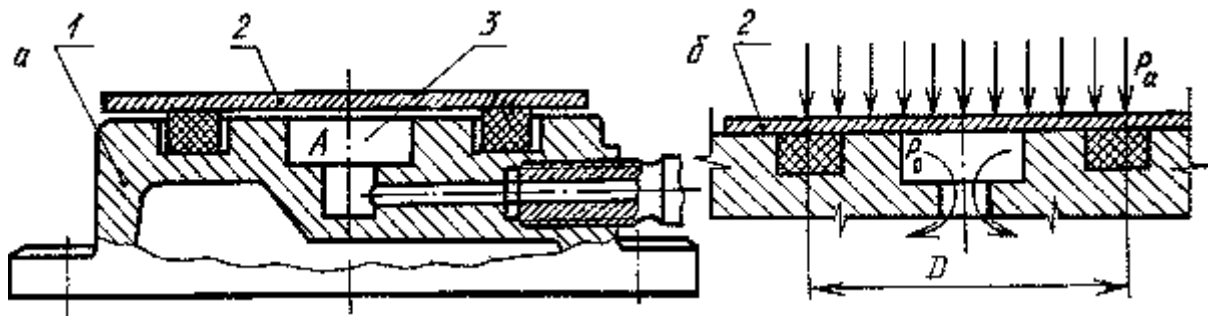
Схема вакуумного приспособления с заготовкой в открытом (а) и прижатом (б) состояниях.
